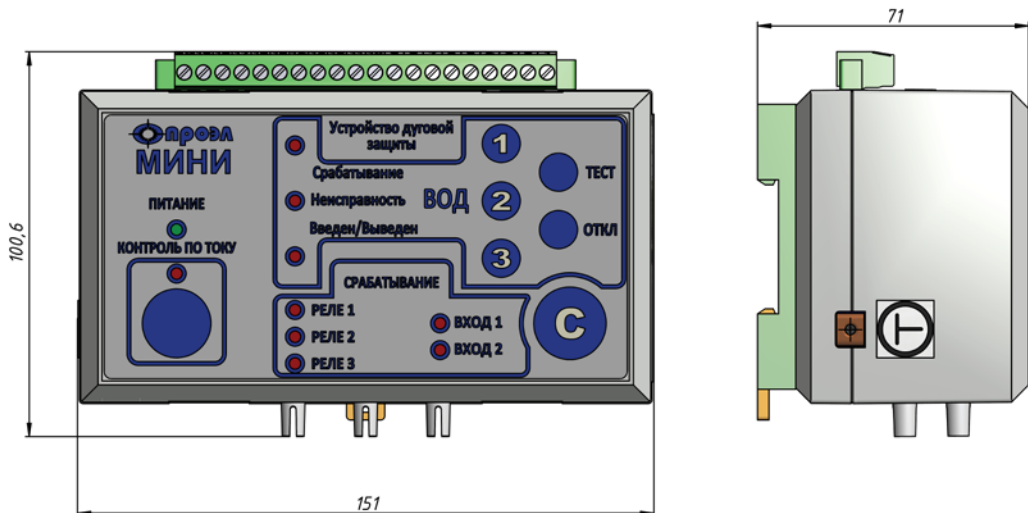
Вид и габаритные размеры БПМ в варианте крепления 01
